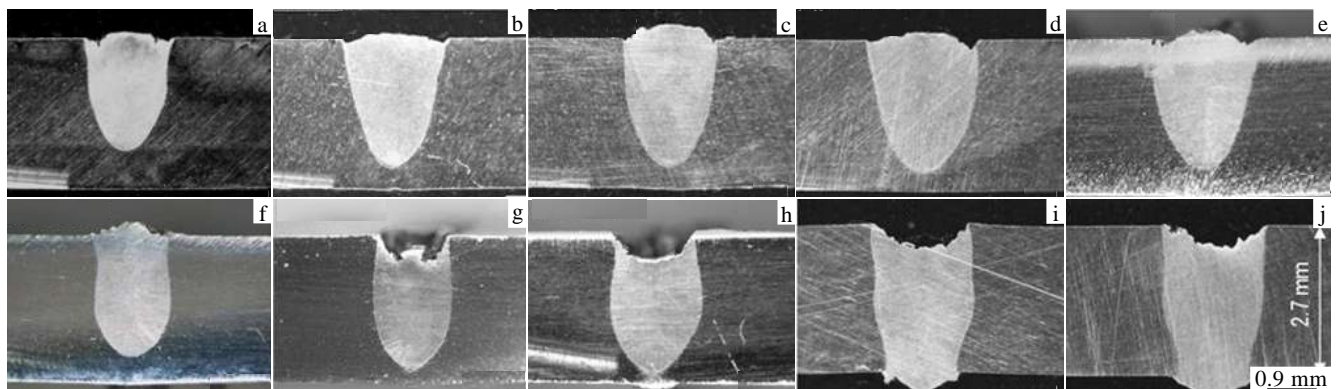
正弦调制焊接 AZ31 焊缝横截面形貌
